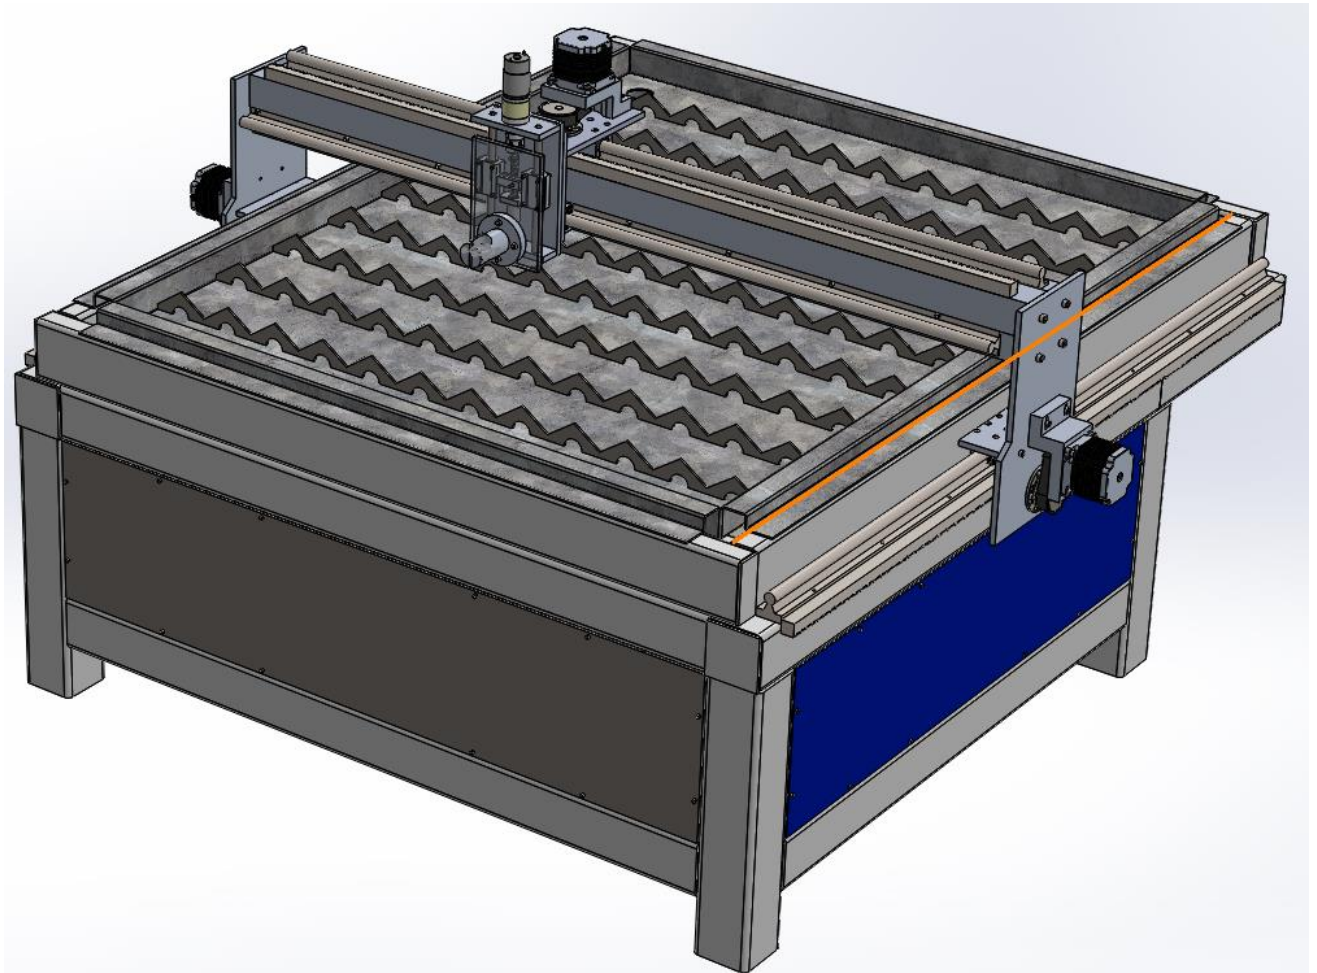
Загальний вигляд 3D-моделі розробленого верстата
